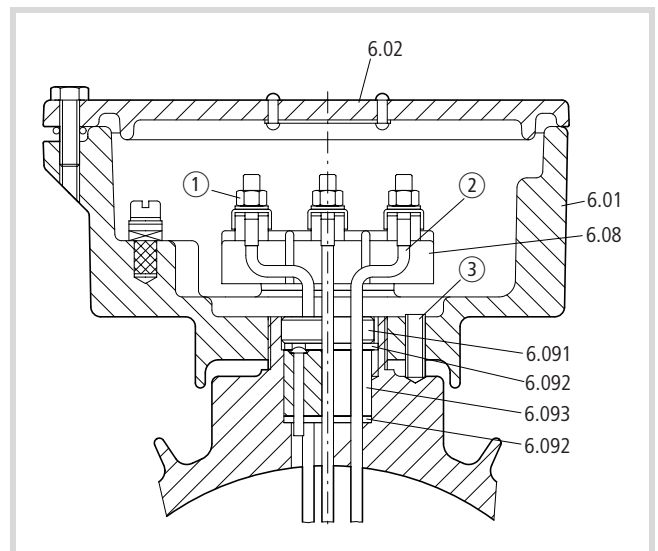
Dévissage des raccordements de la plaque à bornes (6.08)
